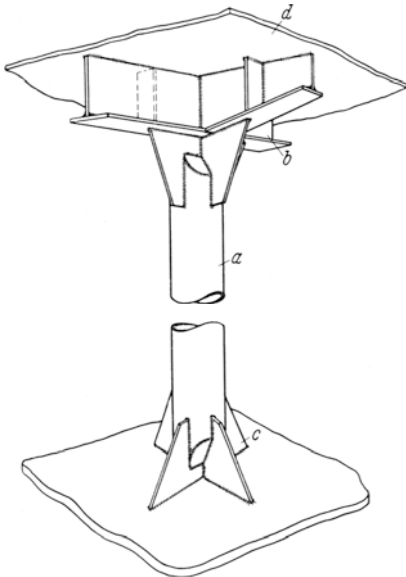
Deckstütze mit geschweißter Kopf- und Fußkonstruktion.
